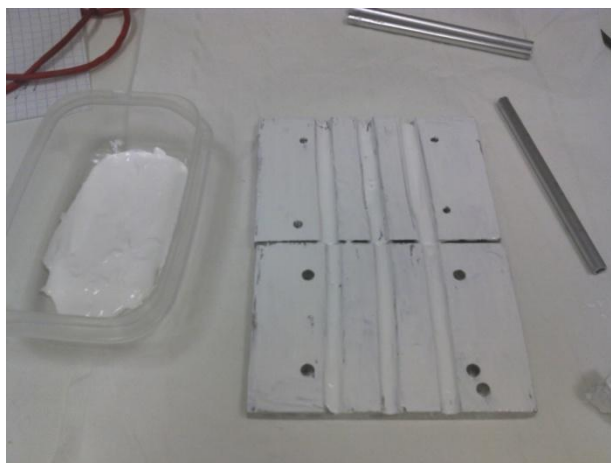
Placa de arrefecimento em construção. Ambas as faces que estarão em contacto com a tubagem foram revestidas com massa térmica, para garantir um fluxo de calor elevado e uniforme.
